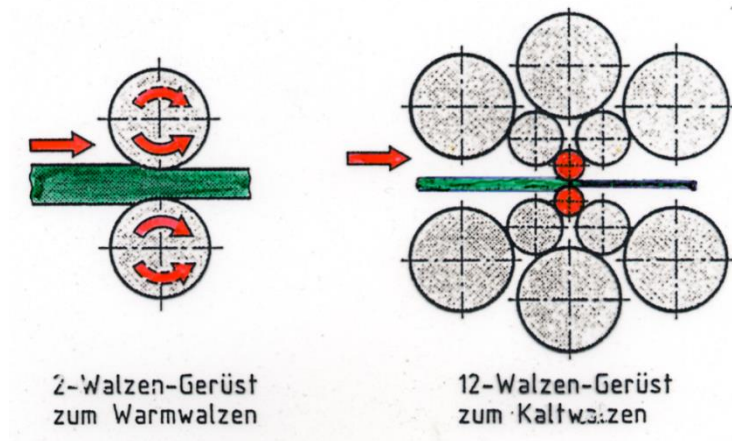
Walzengerüste zum Kalt- und Warmwalzen
